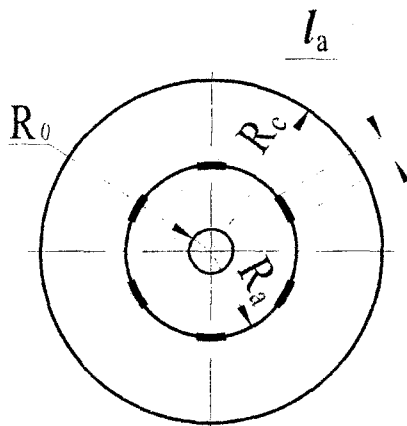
Соединение цилиндрического вала со ступицей по прерывистой поверхности
